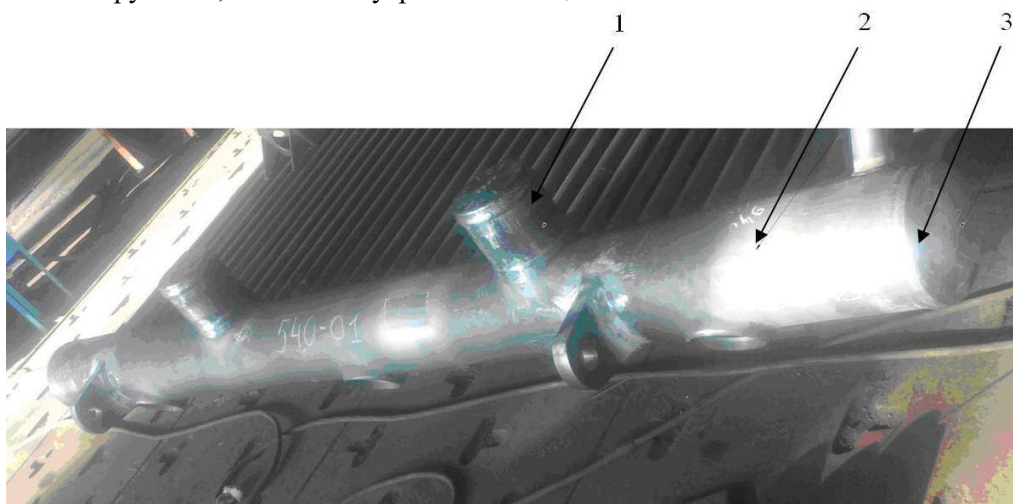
Коллектор в сборе: 1 – патрубок, 2 – корпус коллектора, 3 – доннышко
